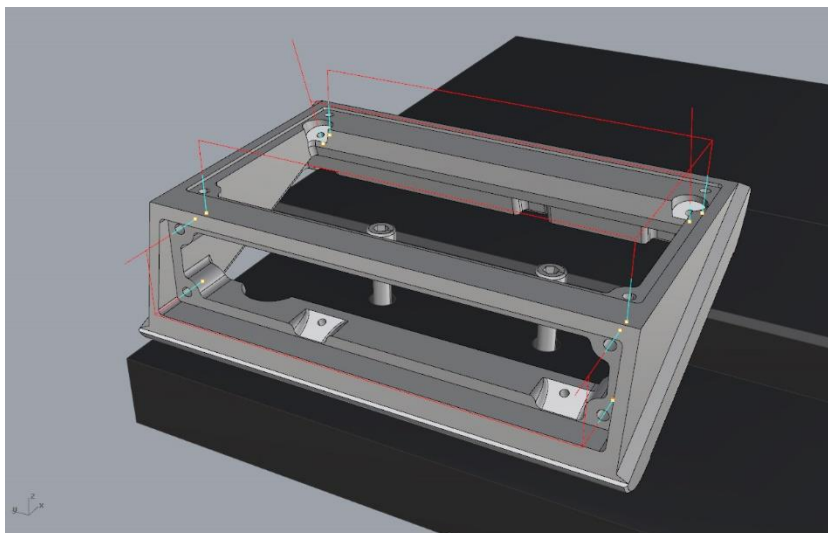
První upnutí – dokončování fréza 4 mm – Parallel Finishing
